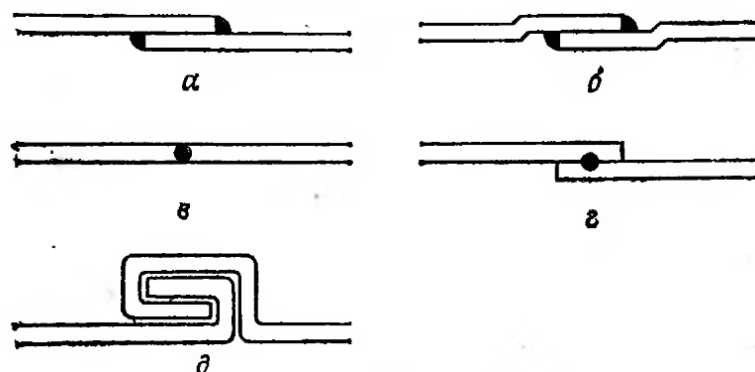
Постійні з'єднання в екранах: а – суцільний зварний шов, б – суцільний зварний шов при ступінчастому з'єднанні ділянок шва, в – шов, отриманий зварюванням встик, г – шов, при точковому зварюванні, шов – внапусток.
